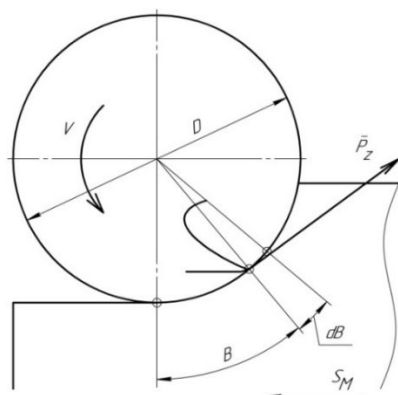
Схема для определения главной (окружной) составляющей силы резания при фрезеровании цилиндрической фрезой
